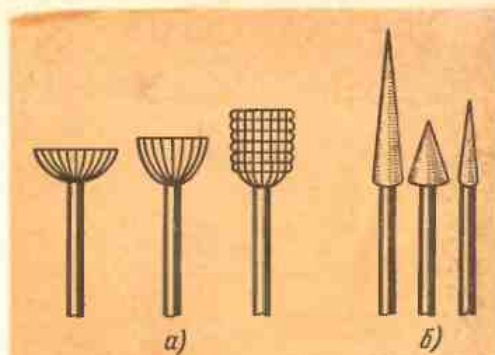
Набор самодельных боров для резьбы рельефа:
